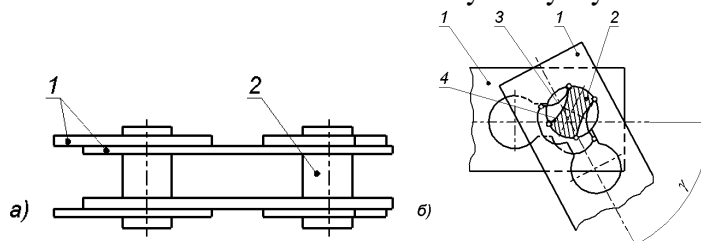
Схема взаимодействия шарнира трения качения с двухсторонним поворотом звеньев цепи: 1 – пластина; 2 – валик; 3 – выпуклая рабочая поверхность отверстия пластины; 4 – вогнутая рабочая поверхность
